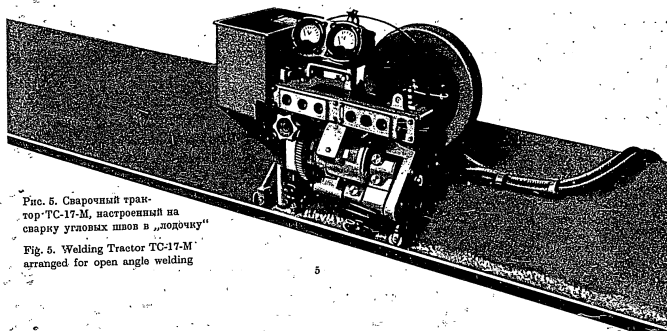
Сварочный трактор ТС-17-М, настроенный на сварку угловых швов в „лодочку“
